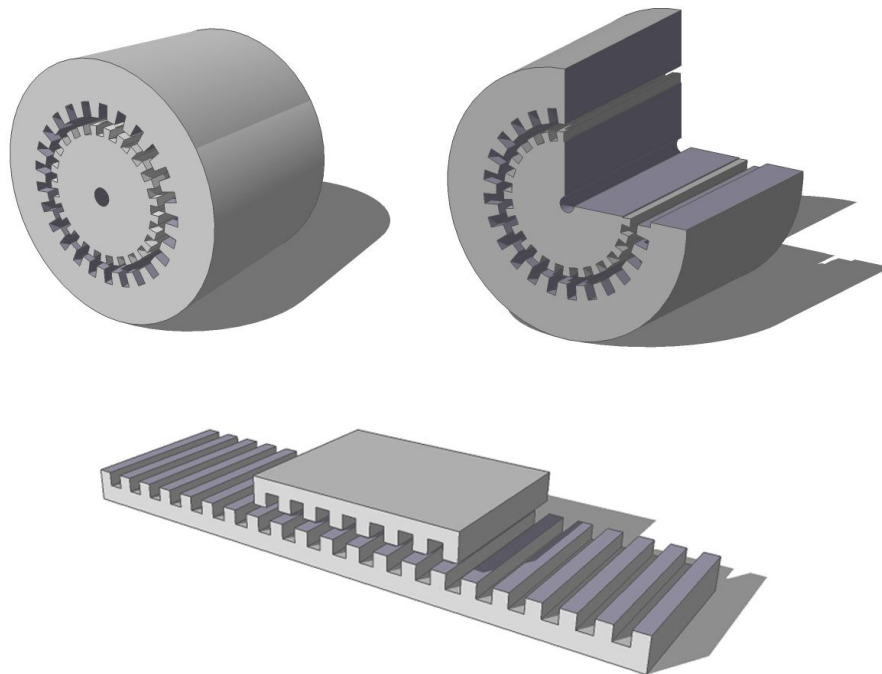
Desenrolamento de um motor tambor para um motor linear.
